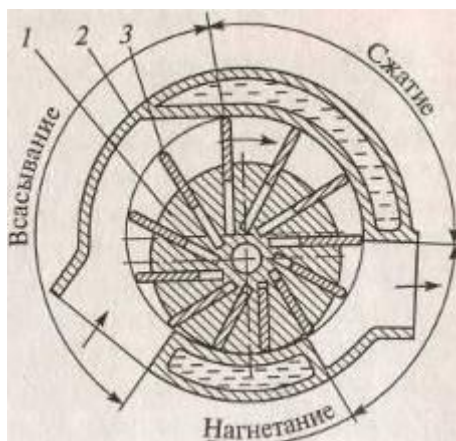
Схема. Роторный компрессор (1 – ротор; 2 – корпус; 3 – пластина)
